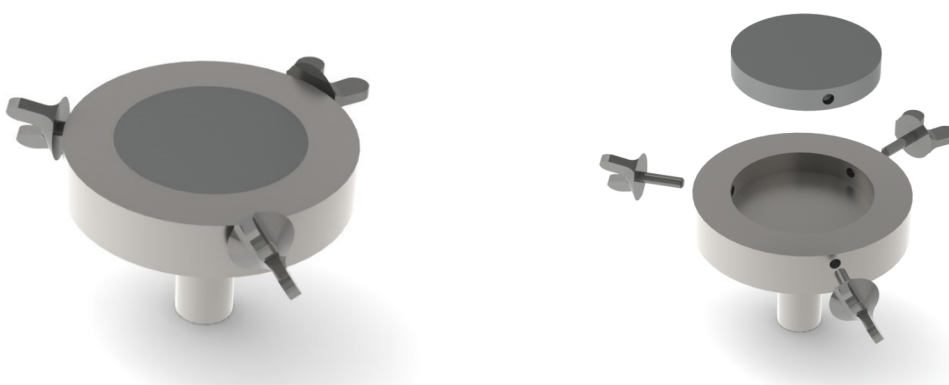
Sistema 1 - vista da montagem e vista explodida.
